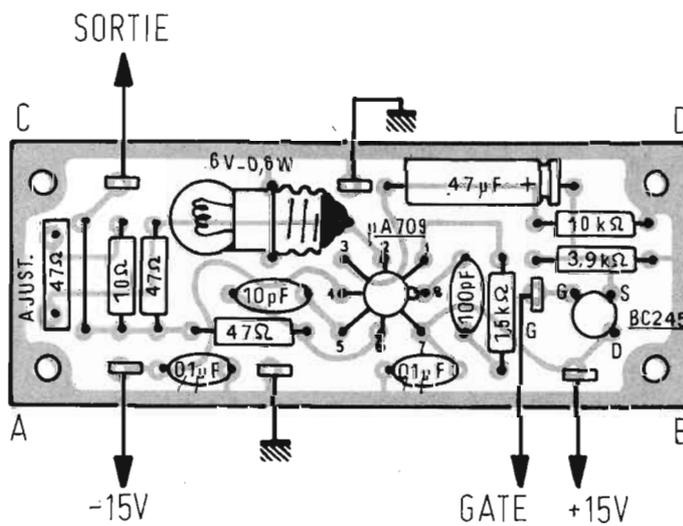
Carte imprimée d'oscillateur expérimental.
